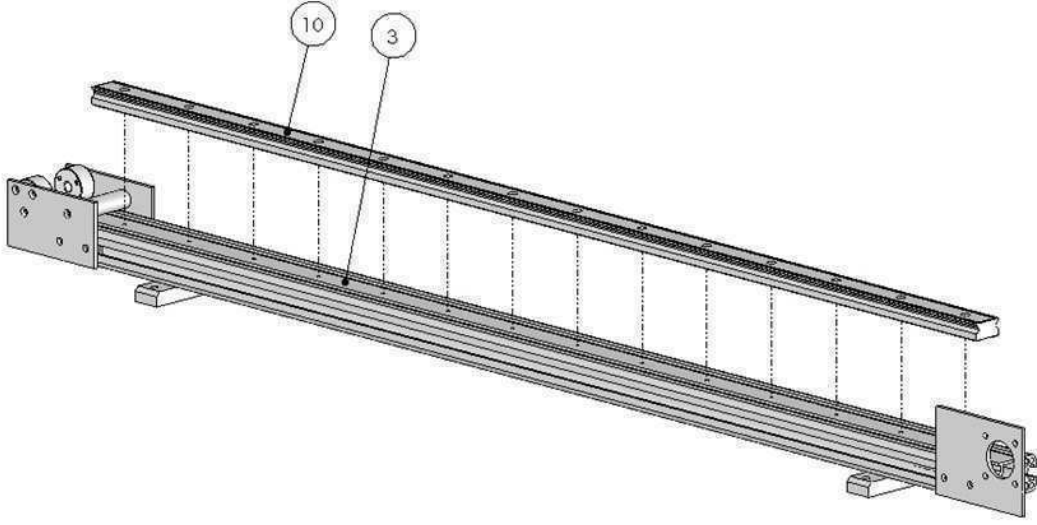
Havşa kafalı M3 vidalar ile destek parçasının montajı
